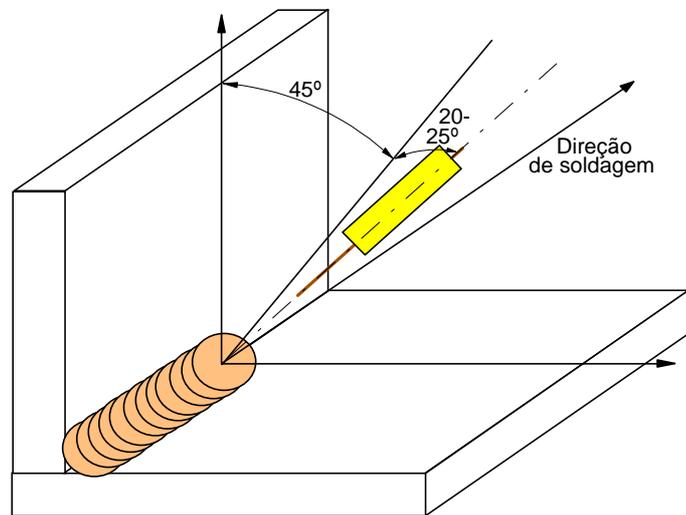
Posicionamento recomendado para a execução de uma solda de filete.
